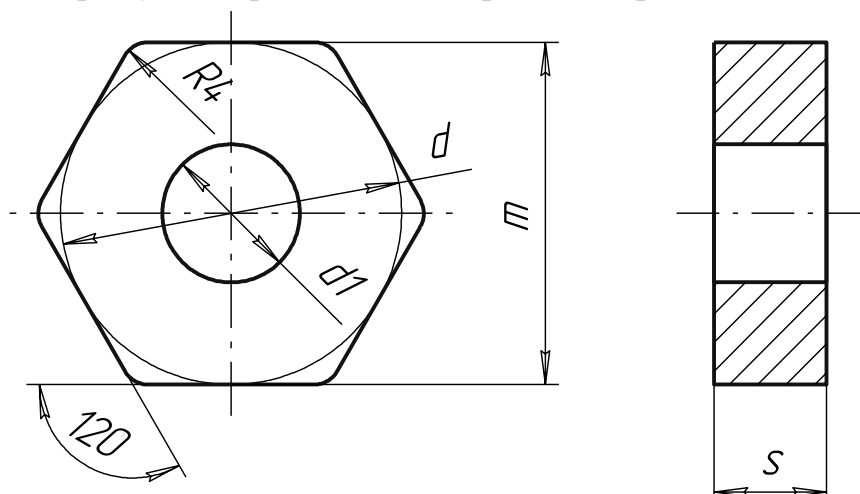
Пластина режущая ГОСТ 19064-80
